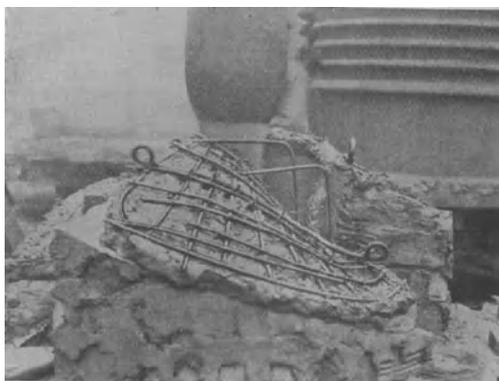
Formen einer Schiffsschraube in Lehm III.
